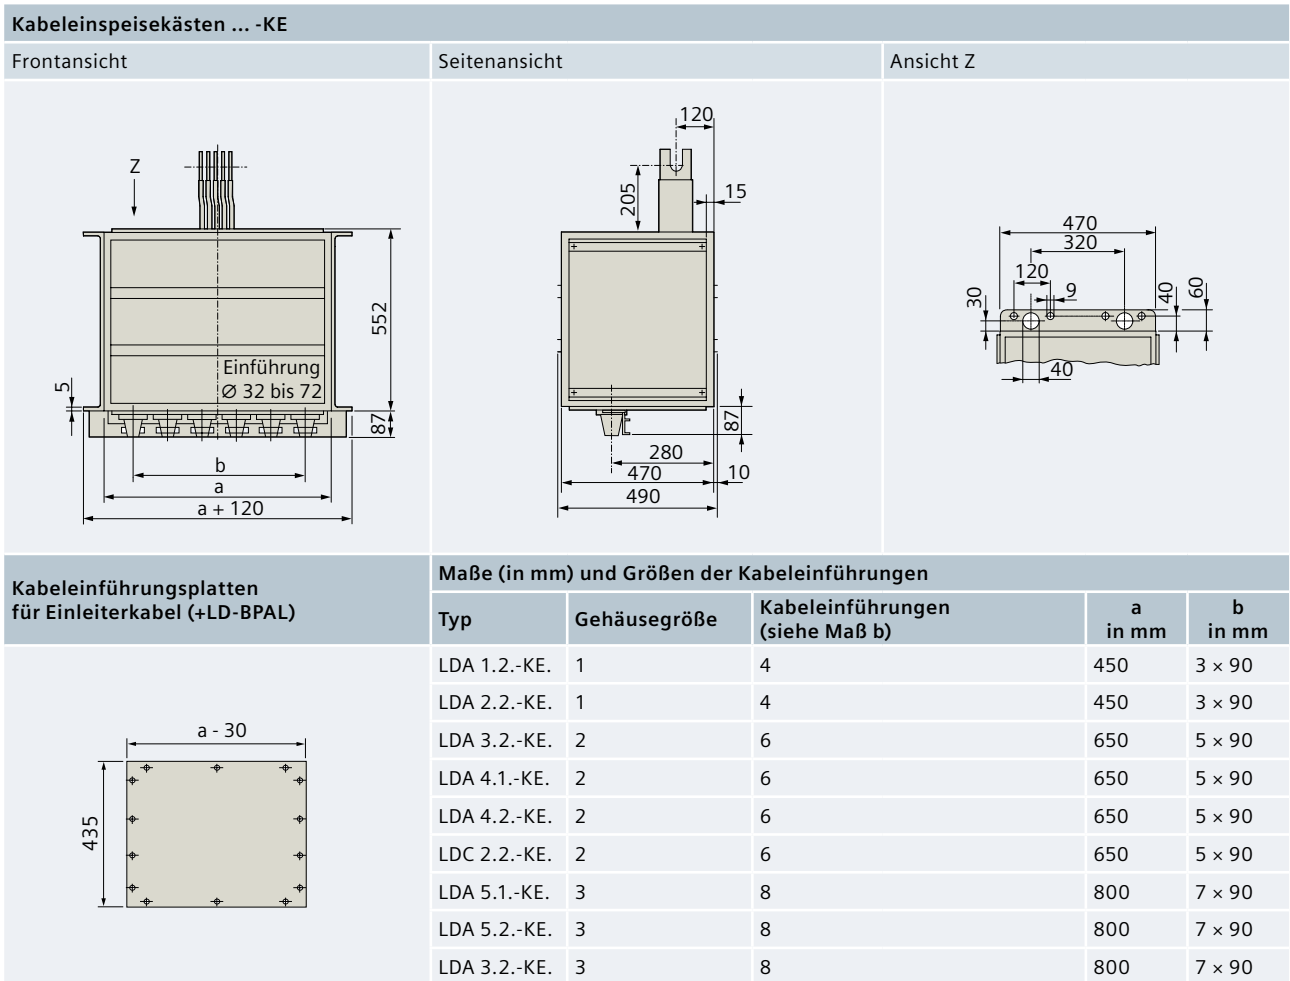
/17: Maße (in mm) und Ansichten für Kabeleinspeisekästen (LD ... -KE.) und die Einführungsplatten für Einleiterkabel (+LD-BPAL)
